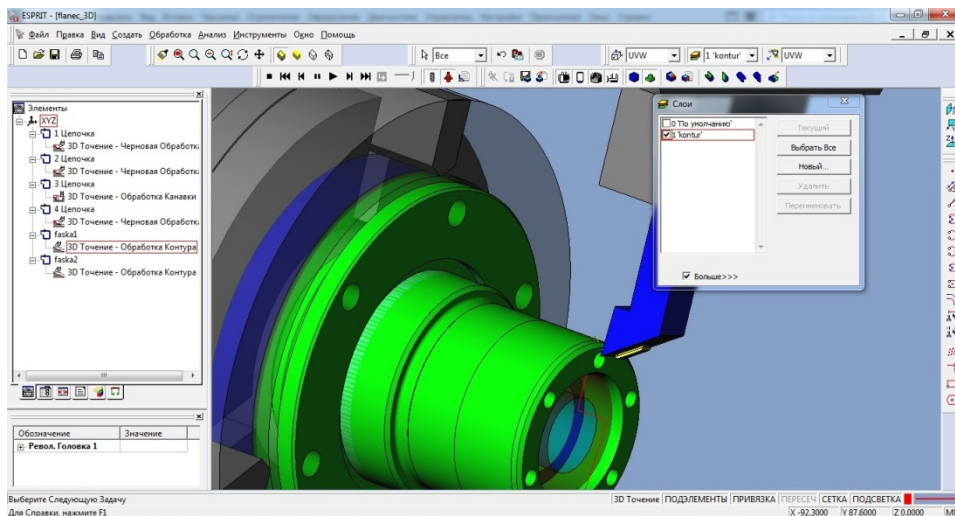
Траєкторія руху металорізального інструменту при обробленні контуру вала-шестерні
